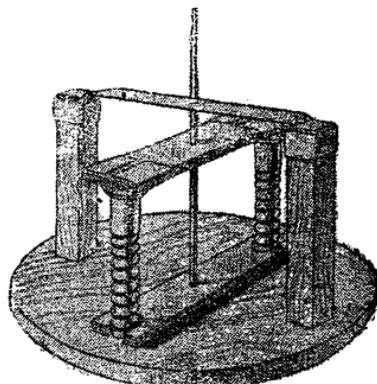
Так должны стоять шурупы под якорем. Здесь же видна форма соединительных полосок.
